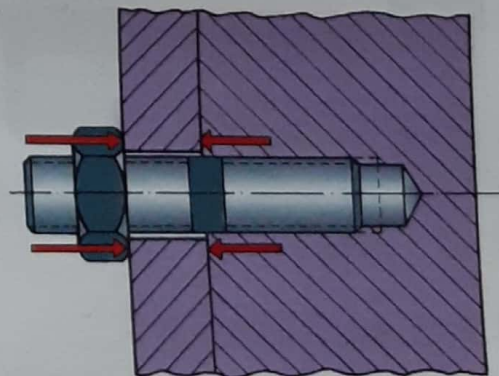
Ensamblaje atornillado mediante tornillo sin cabeza, tuerca y la pieza.
